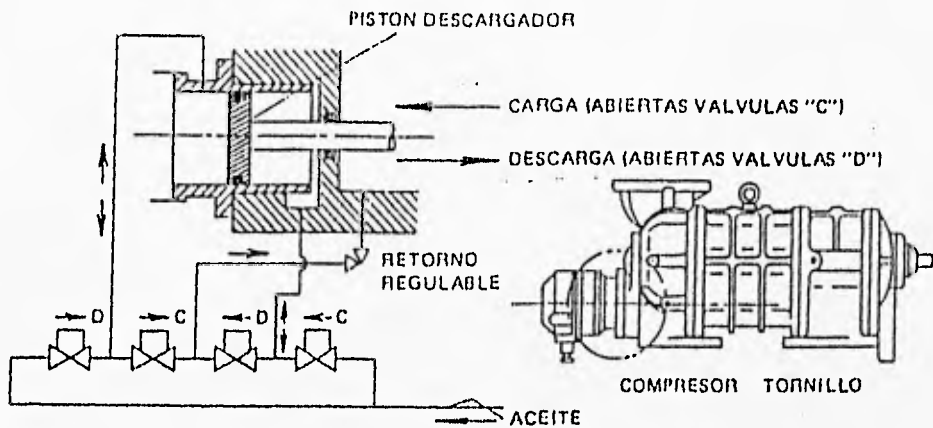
DETALLE DEL PISTON DESCARGADOR DEL CONTROL DE CAPACIDAD DE UN COMPRESOR TORNILLO.
